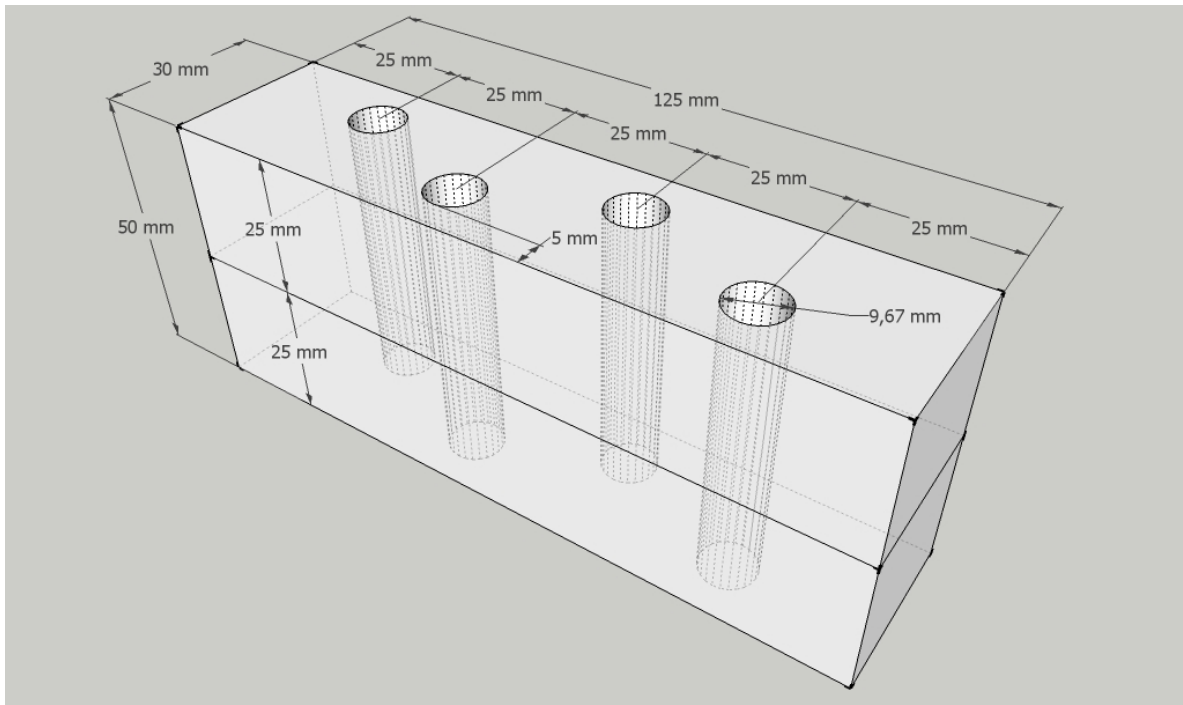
Schéma et dimensions d'assemblage soudé pour les essais en traction linéaire.
